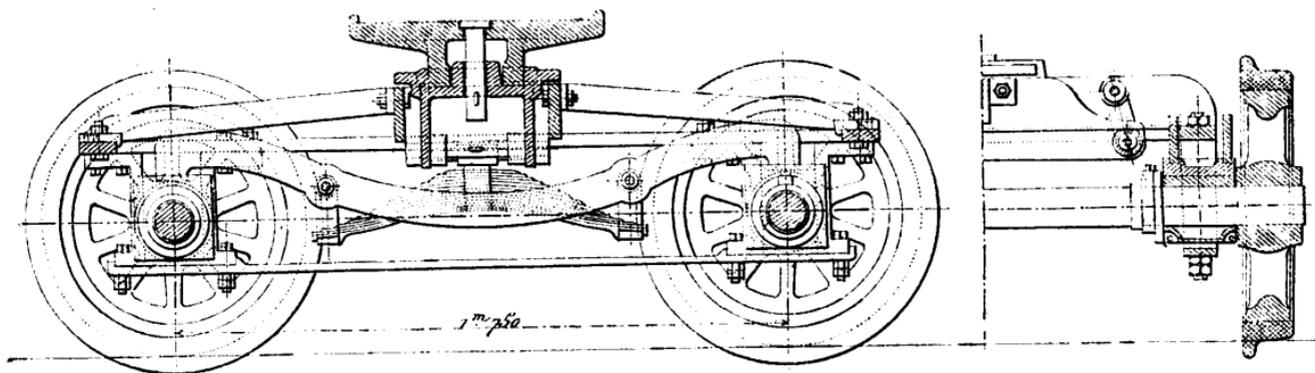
Bogie à suspension par bielles inclinées ; coupe longitudinale par l'axe du pivot, et coupe transversale par l'axe d'un essieu.
